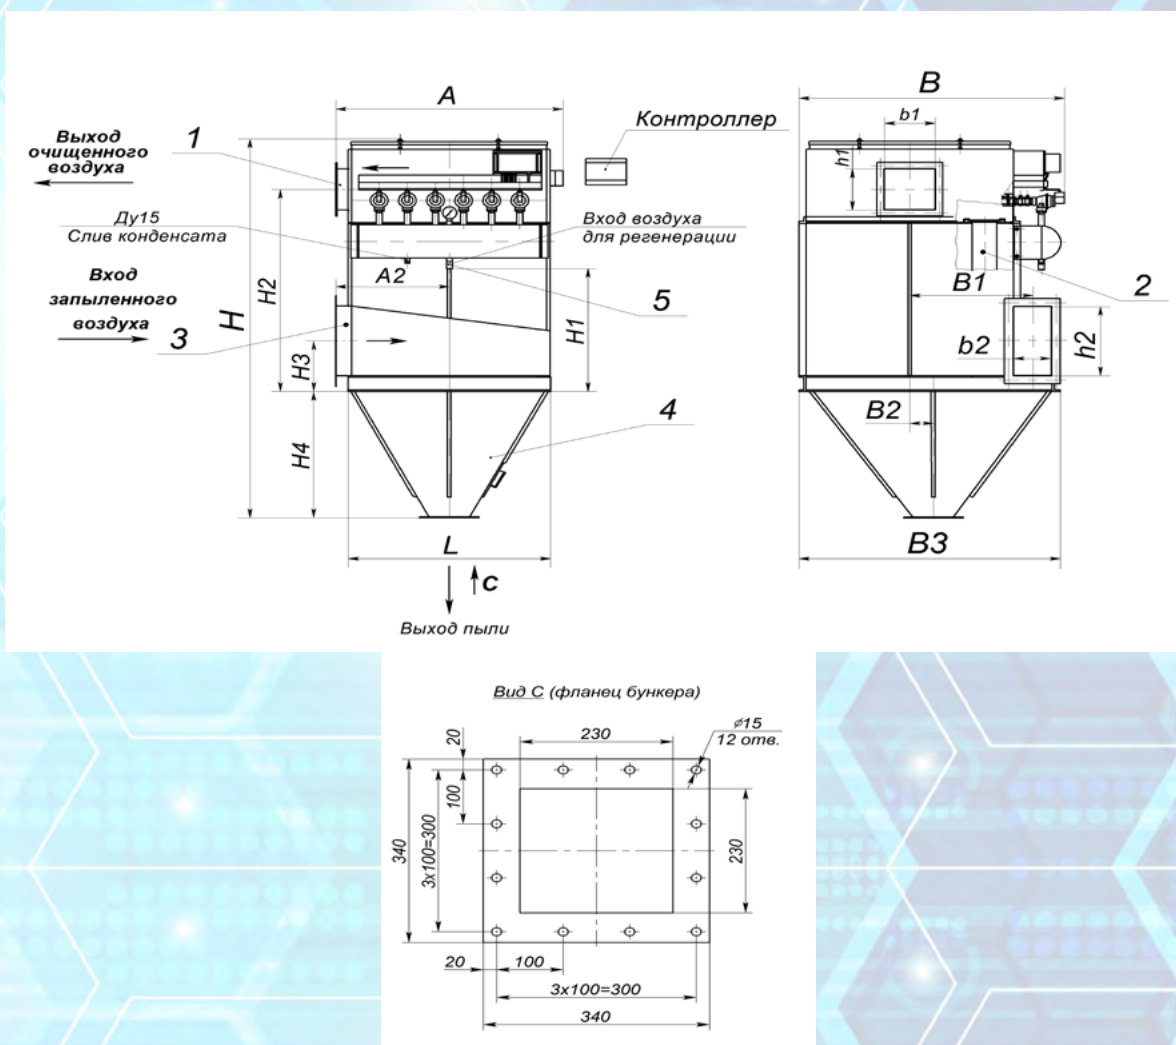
Схема фильтров рукавных типа ФРИП-5; ФРИП-10; ФРИП-15; ФРИП-30; ФРИП-180
